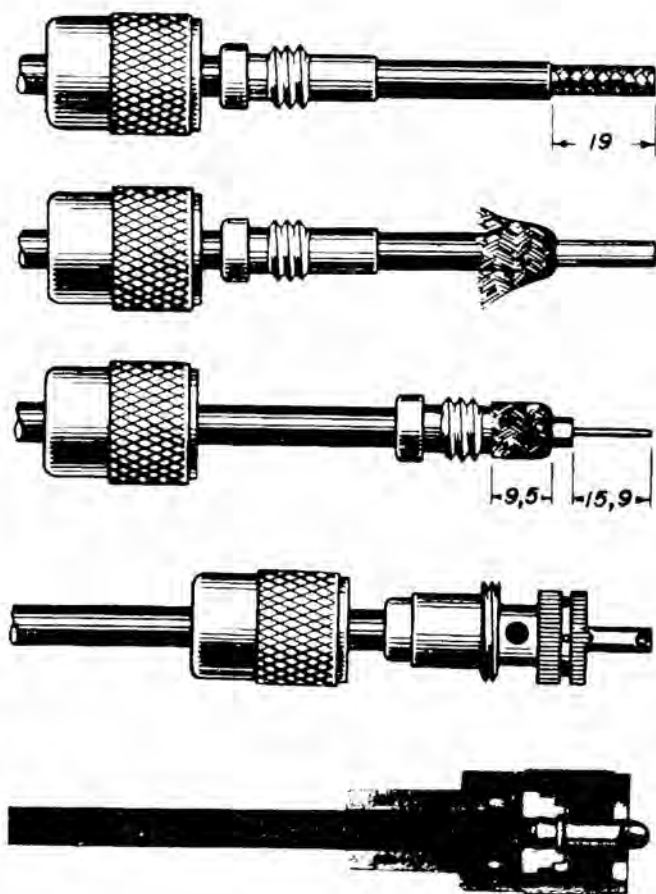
Montagem de um conector QM2 na extremidade de um cabo coaxial, com adaptador QA1. Cortesia da Whinner S.A. Indústria e Comércio. (Cotas em milímetros.)
